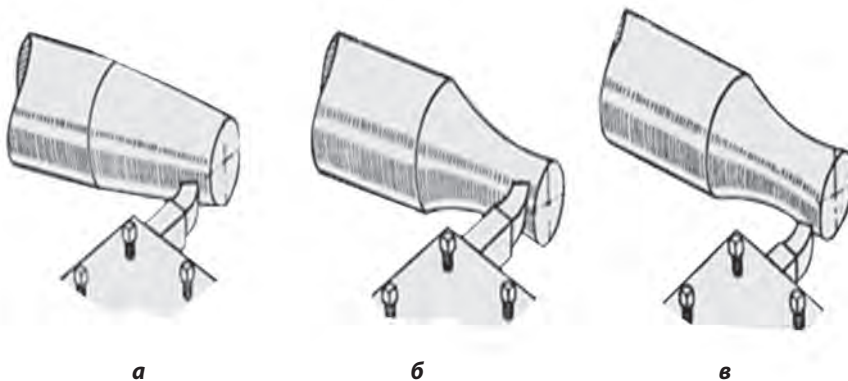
Установка різця при обточуванні кінчної поверхні:
